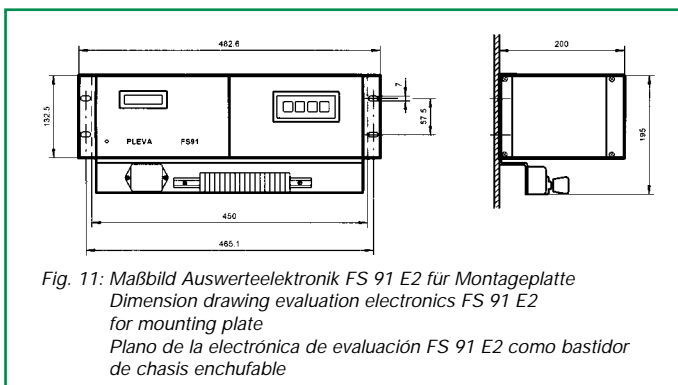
Maßbild Auswerteelektronik FS 91 E2 für Montageplatte
